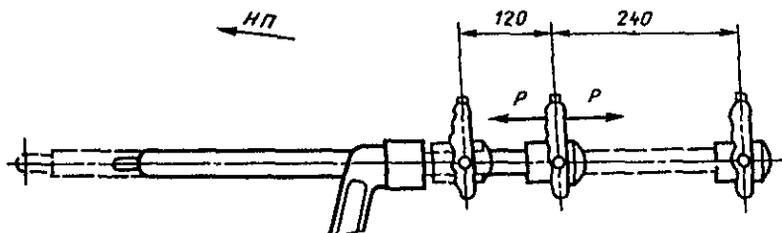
Схема проверки усилий перемещения руля высоты
